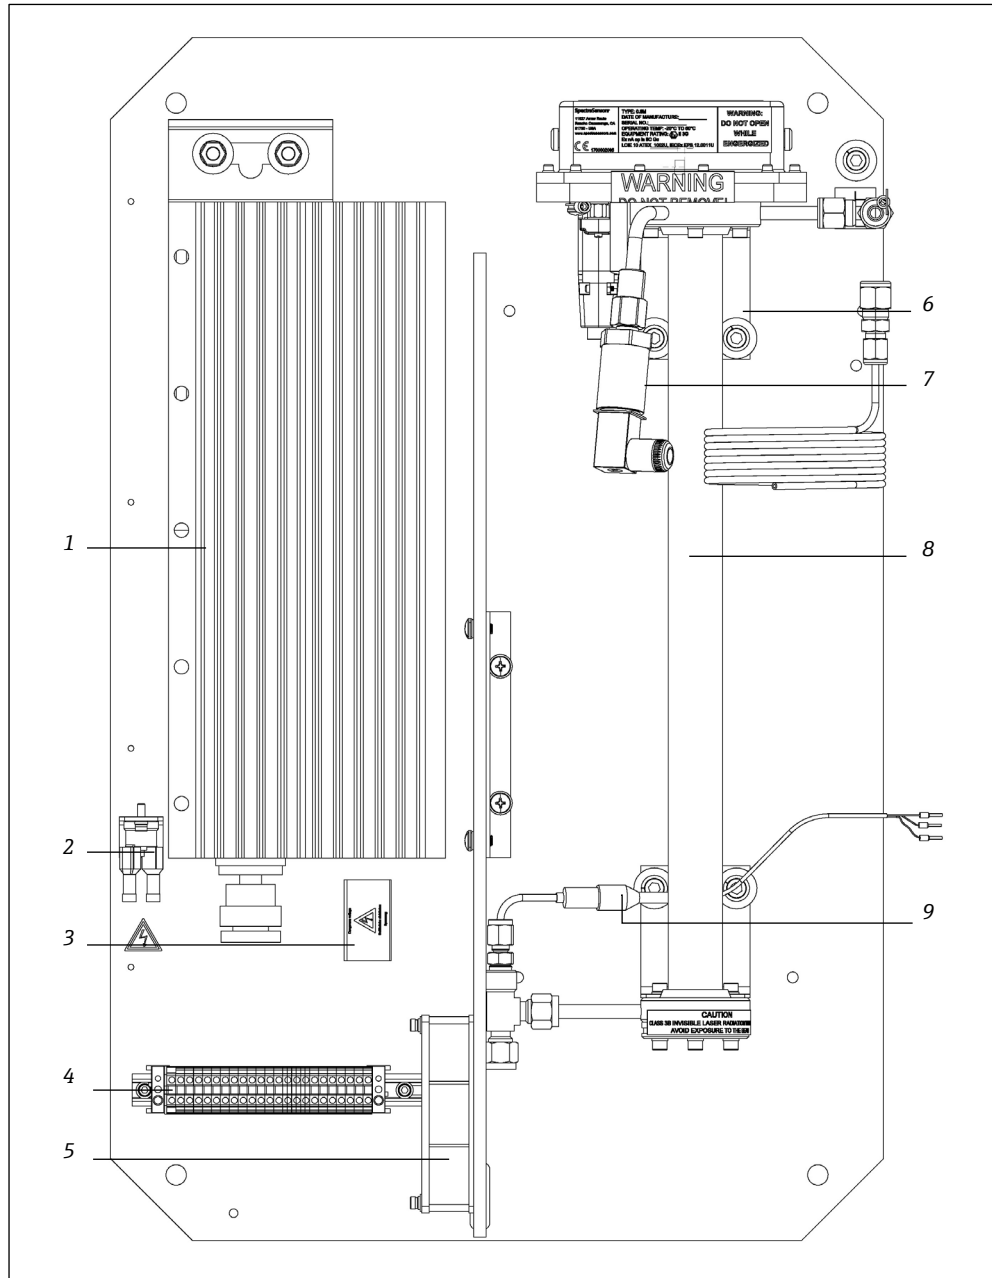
Komponenten auf einer 0,8m-Messzellenbaugruppe
